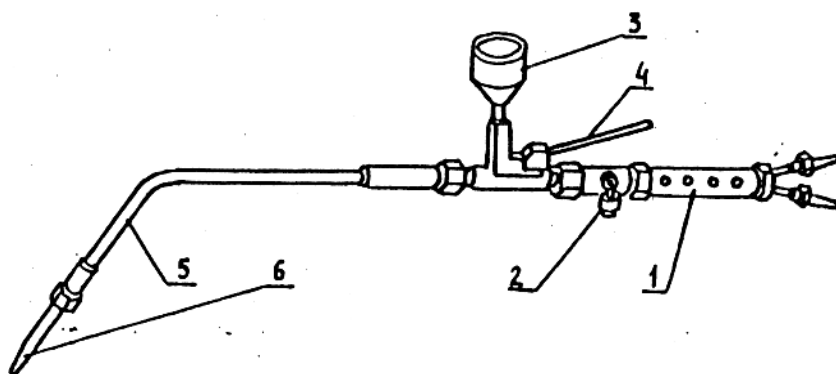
Пальник для газопорошкового наплавлювання: 1)- корпус; 2)- вентиль; 3) – контейнер для порошку; 4)- ручка; 5)- трубка; 6)- мунштук.
